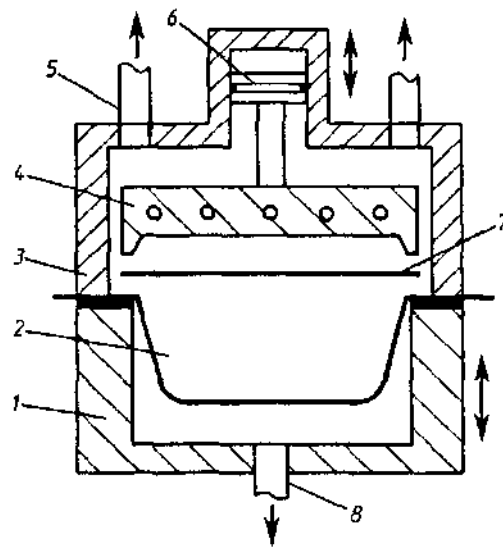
Схема вузла запечатування: 1 – камера, 2 – ємність; 3 – кришка, 4 – штамп; 5, 8 – патрубки для вакуумування; 6 – поршень пневмоциндра; 7 – верхня плівка
